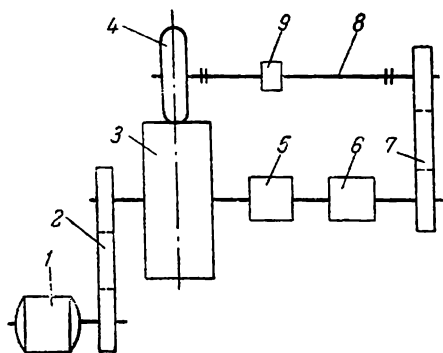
Схема станка для обкатки шины с передачей крутящего или тормозного момента:
